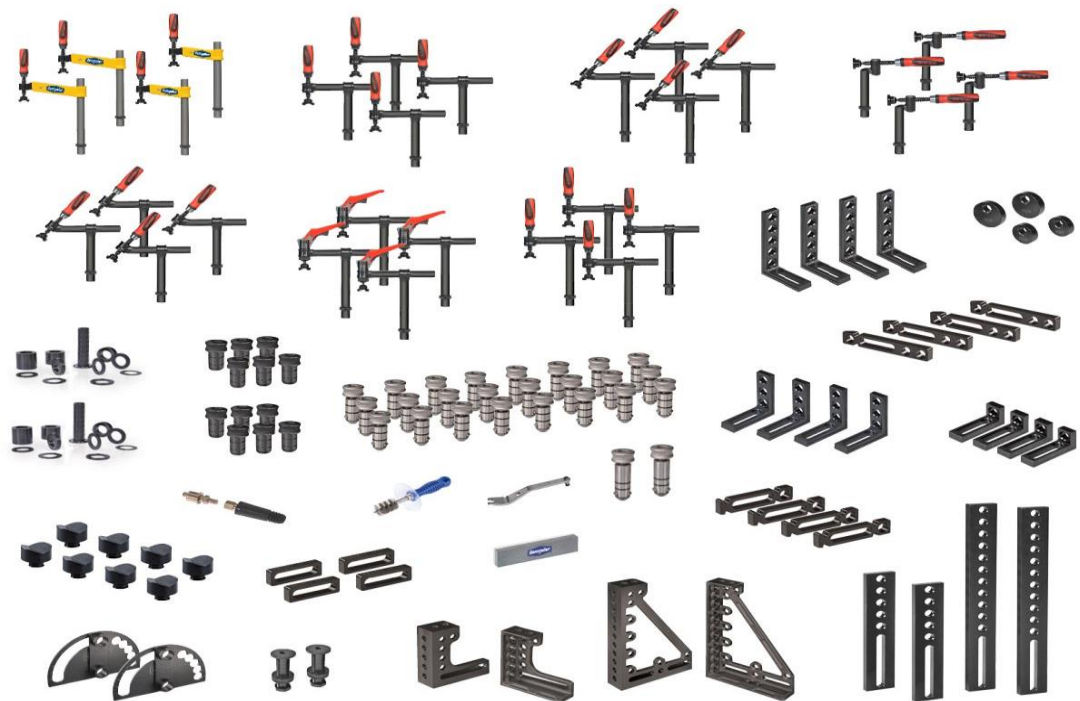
Крепежные элементы сборочно-сварочного стола
